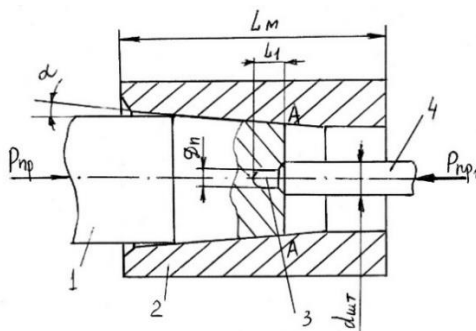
Схема зацентрування заготовки: 1 – заготовка; 2 – матриця; 3 – пуансон; 4 – шток гідроциліндра
